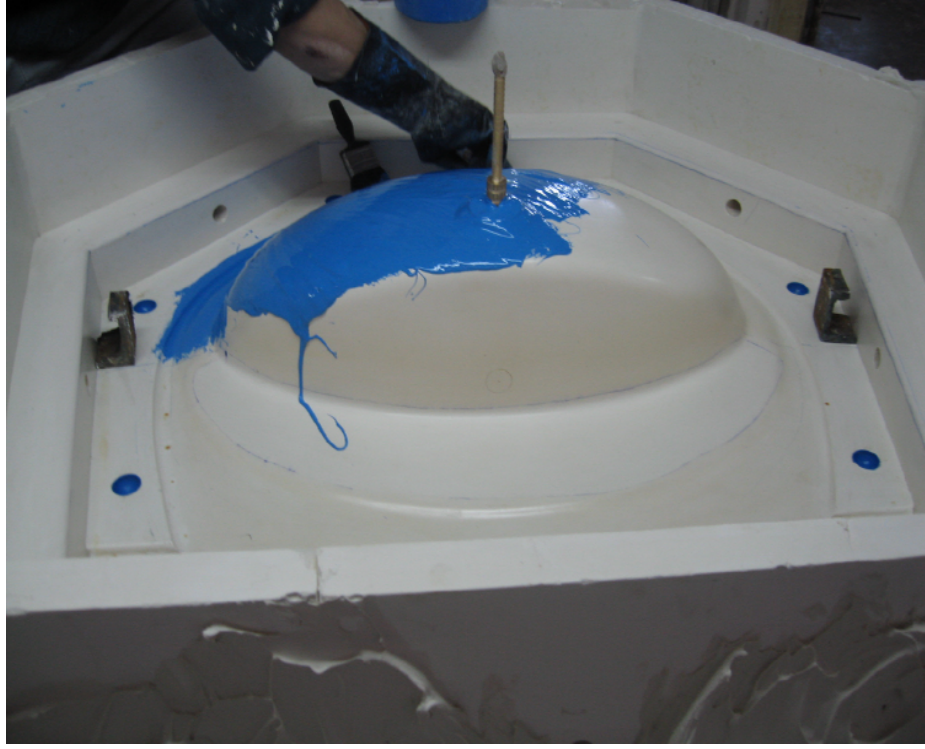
Yan enayi ceketlerin oluşturulması
